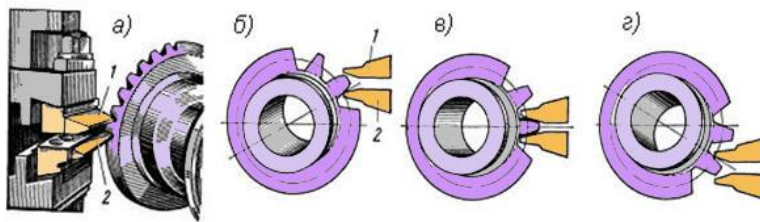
Нарізування конічного зубчастого колеса на зубостругальний верстаті
